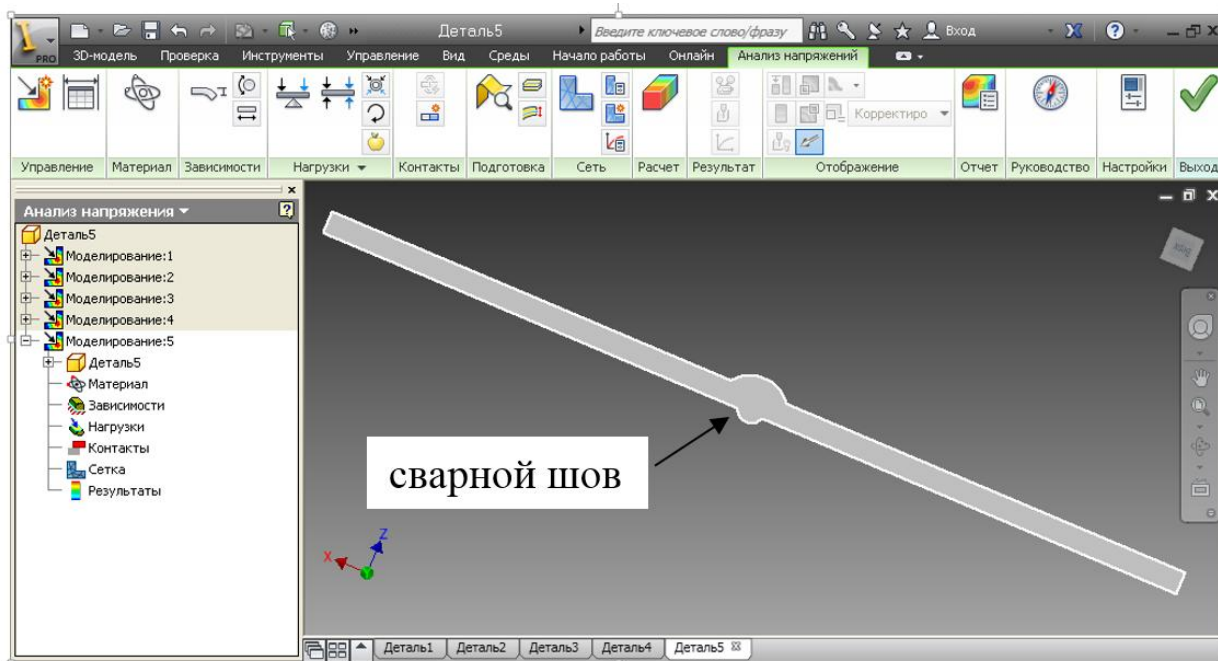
Общий вид (профиль шва) сварной конструкции из 2-х пластин
